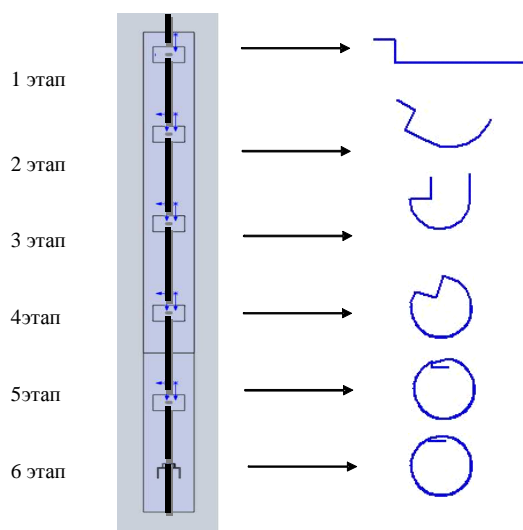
Этапы формирования сварочной проволоки.
